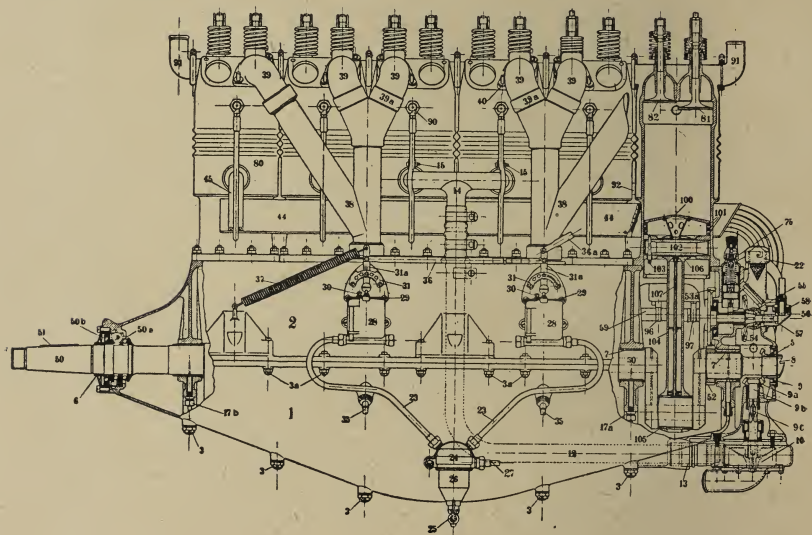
Sechszylinder-Benz-Flugmotor (Längsschnitt).
